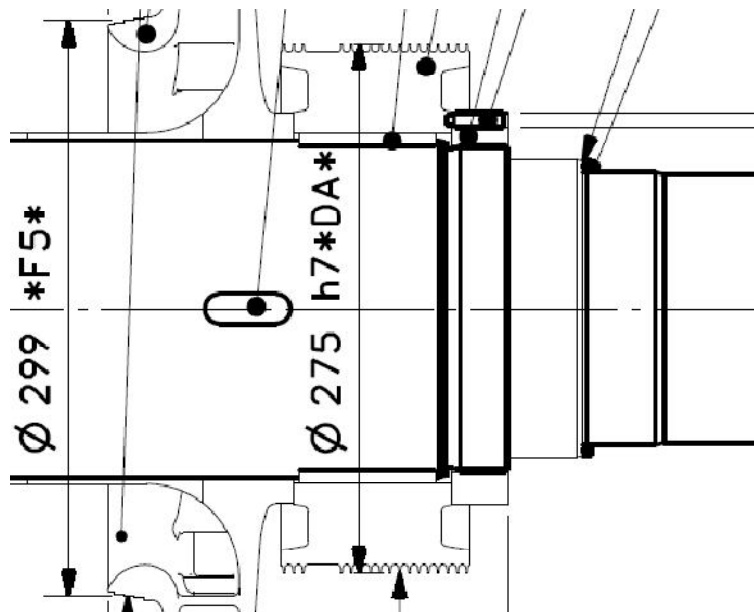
Dimensions du piston d'équilibrage du compresseur 3BCL455
